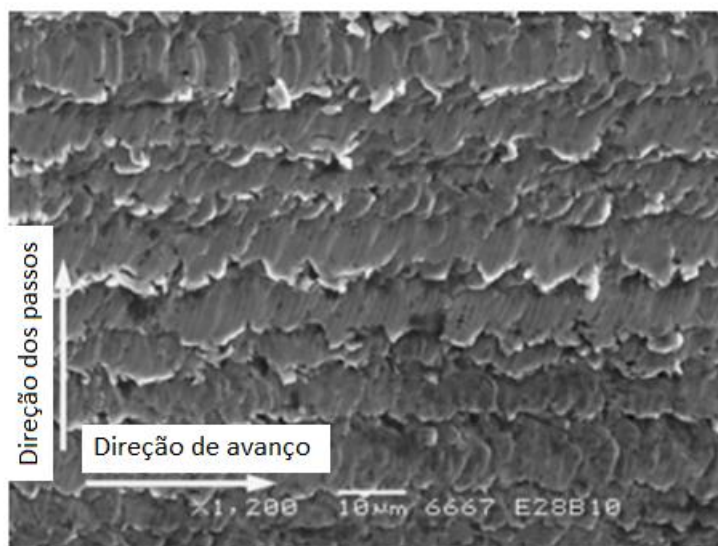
Superfície usinada em aço ferramenta (Adaptado de [2])
